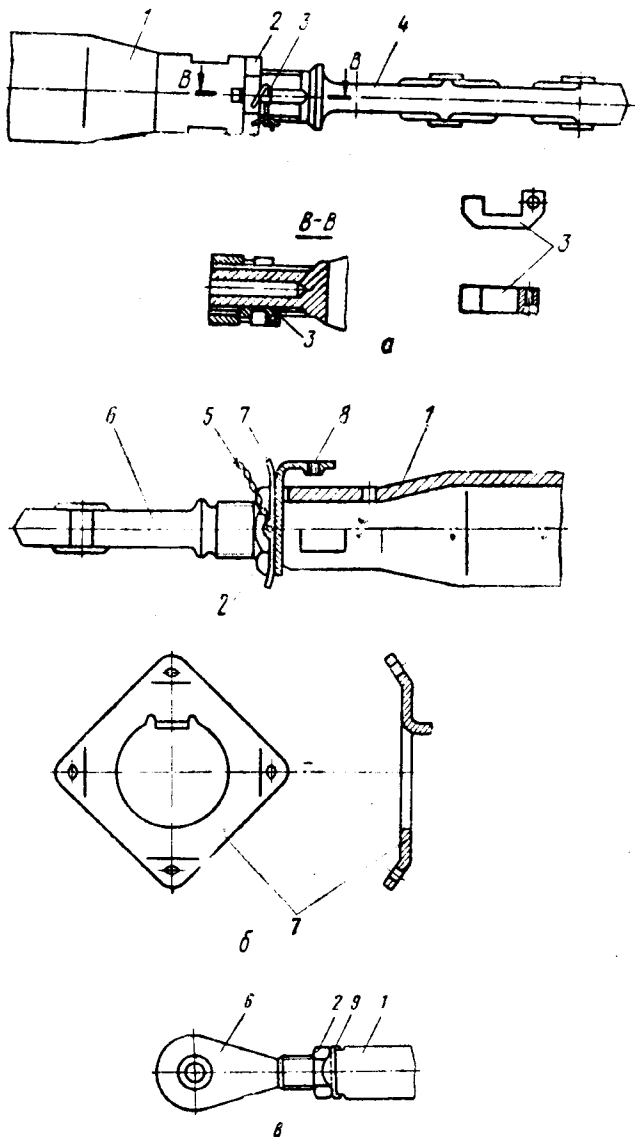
Контровка регулируемых наконечников тяг: а — контровочной шпонкой и гайкой; б — двумя шайбами и гайкой; в — шайбой и гайкой, 1 — труба; 2 — гайка; 3 — шпонка контровочная; 4 — наконечник ушковый сдвоенный; 5 — контровочная проволока; 6 — наконечник ушковый; 7, 9 — шайба контровочная; 8 — шайба по ОСТ 1.12804—77.
